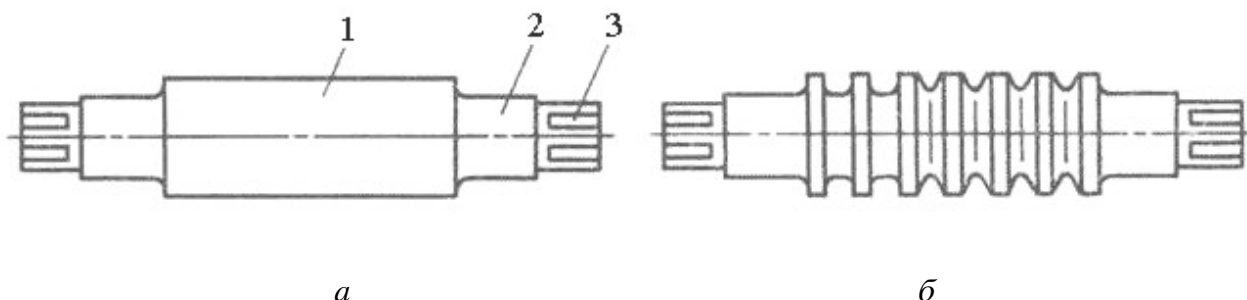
Прокатные валки: а – гладкий: 1 – бочка; 2 – шейки; 3 – тrefь; б – калиброванный
